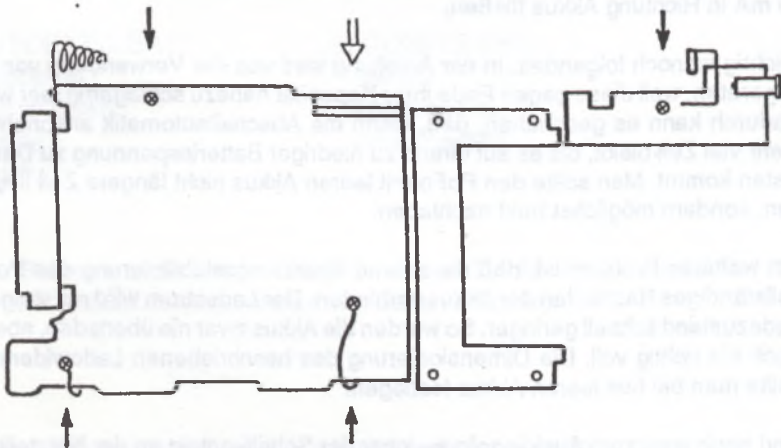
Portfolio-Hauptplatine. Die Pfeile zeigen auf die Schrauben.
